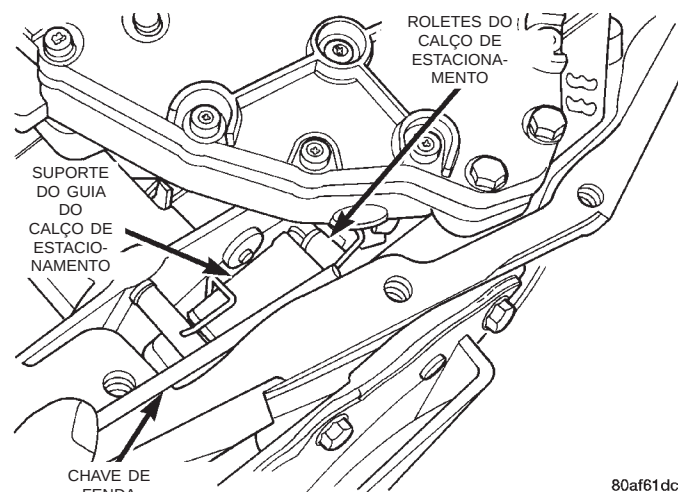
Remoção dos Roletes da Haste de Estacionamento do Suporte da Guia
